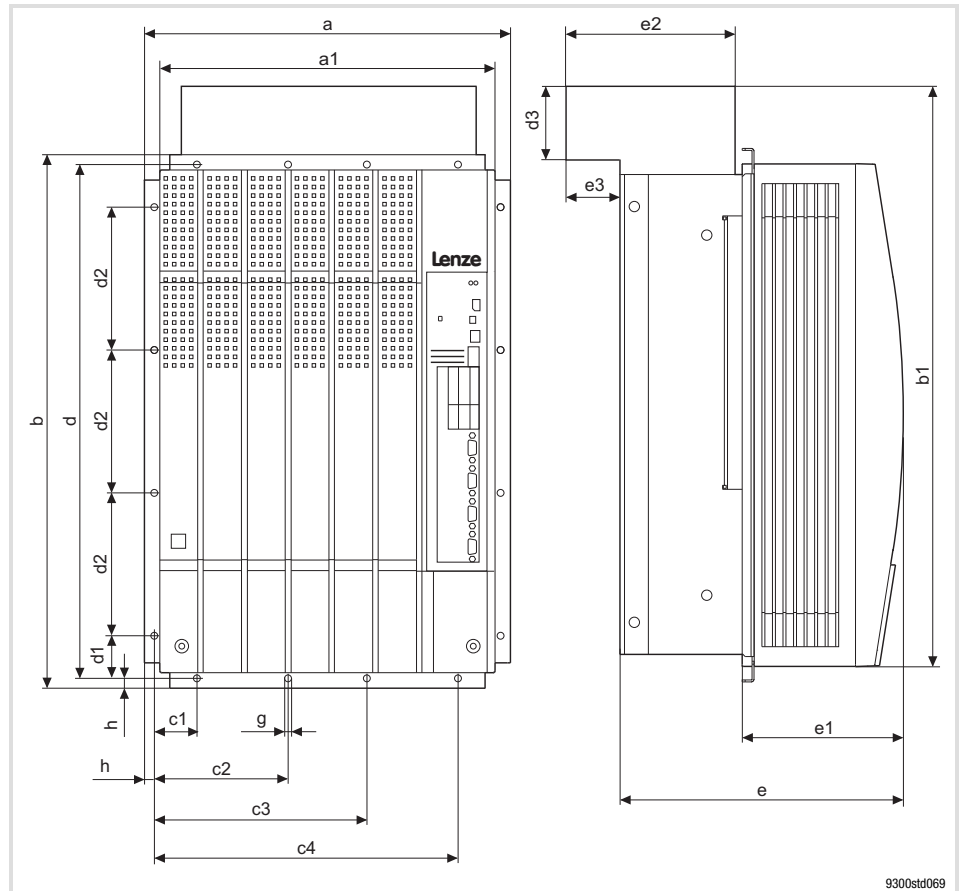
Abmessungen Montage thermisch separiert 45 kW
